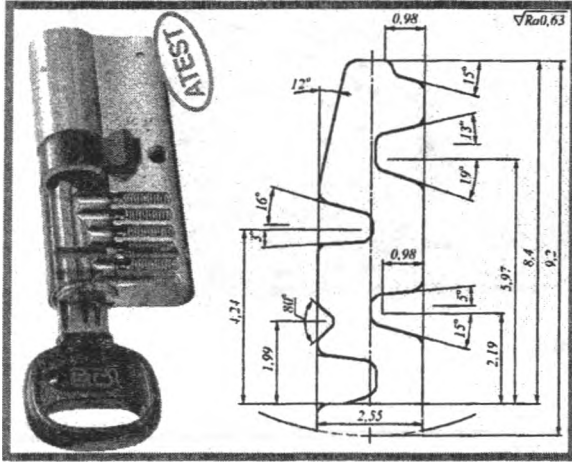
Внешний вид вкладыша и типового профиль паза (приведены номинальные размеры)
